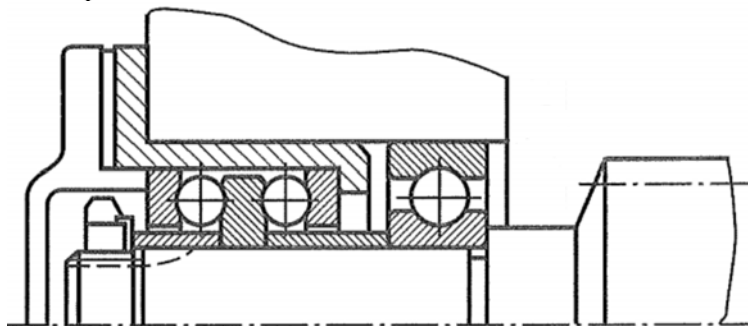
Варианты конструкции фиксирующей опоры с комбинацией шарикового упорного двойного подшипника с радиальным шариковым подшипником
